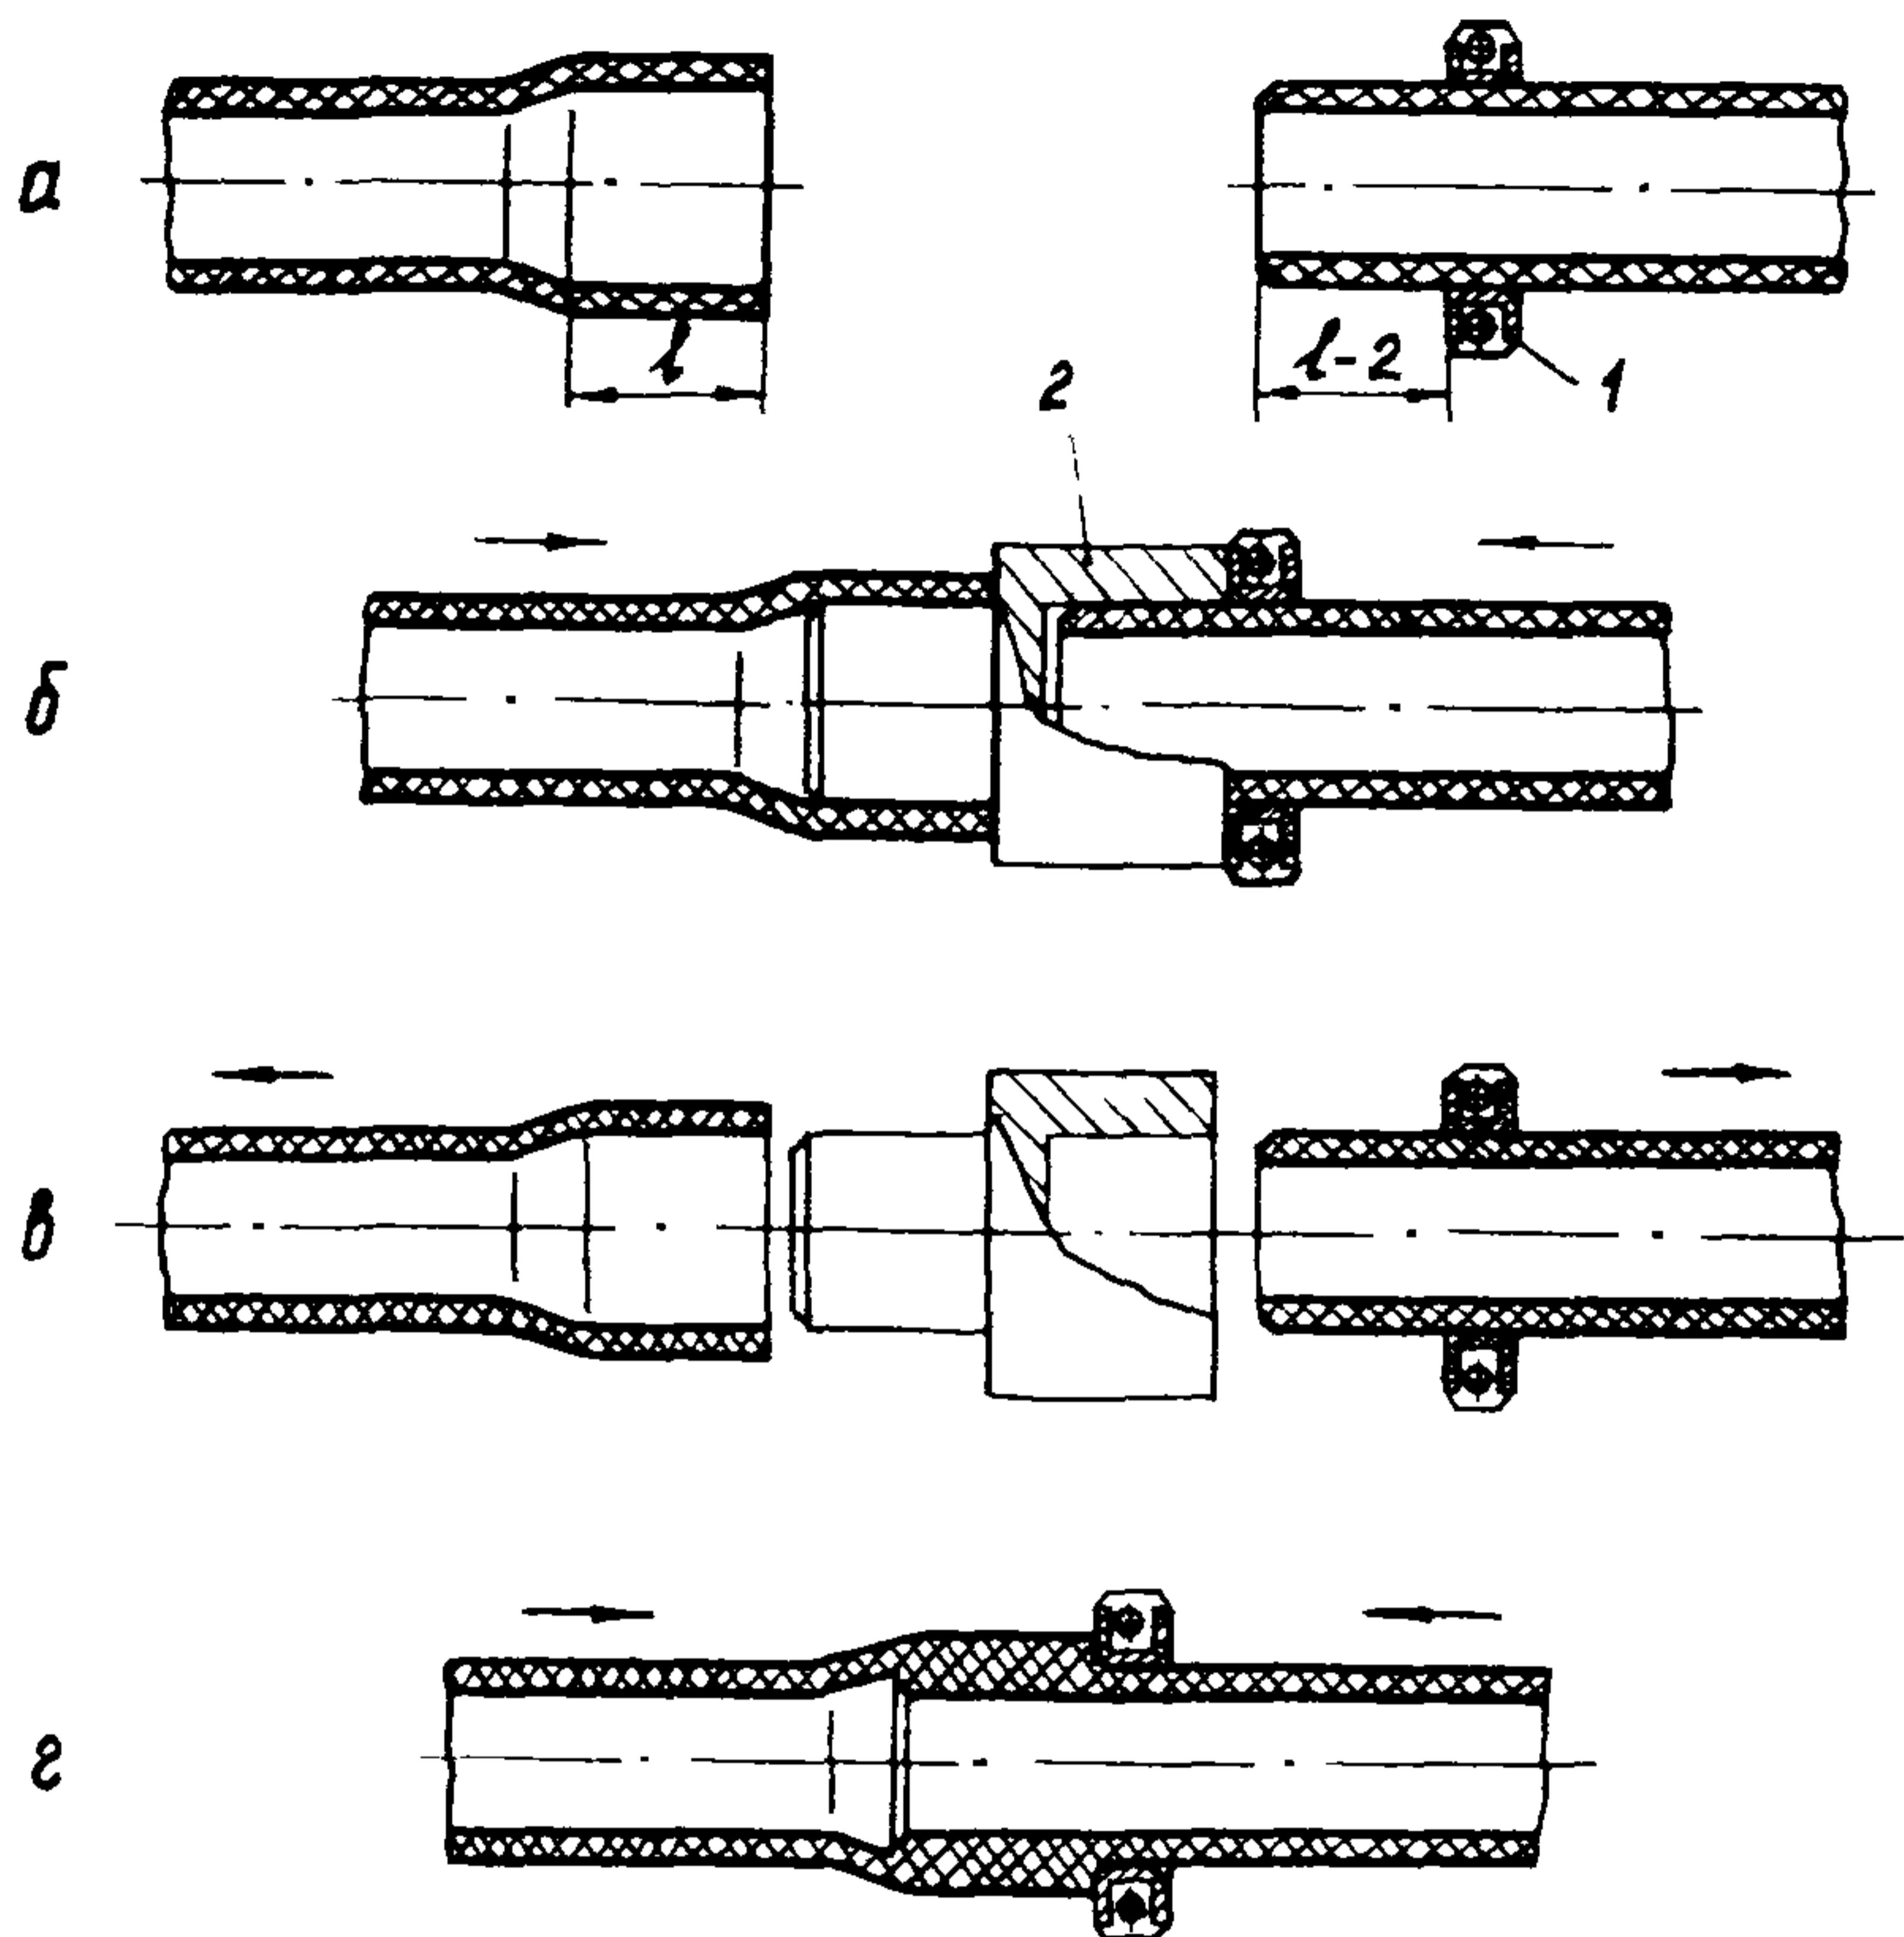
Последовательность процесса контактной тепловой сварки враструб труб из полиэтилена:
